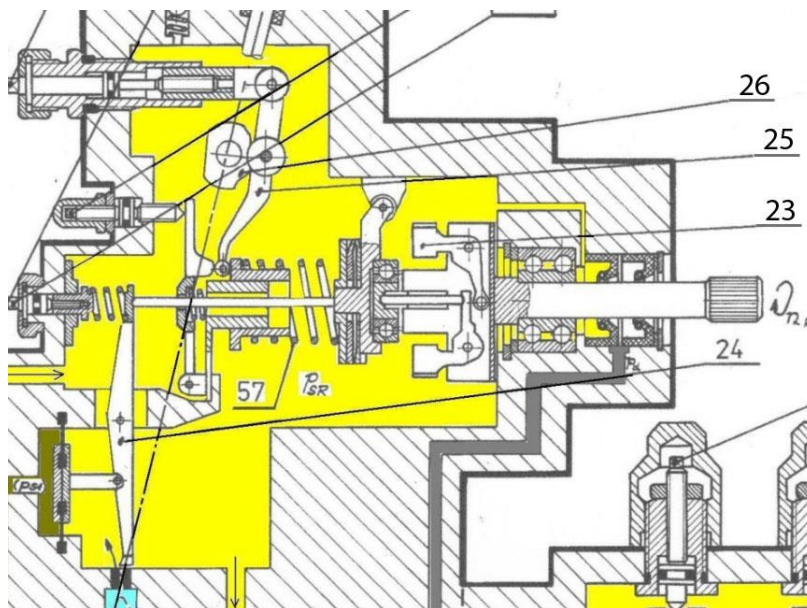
Řízení dodávky paliva do motoru [6]
